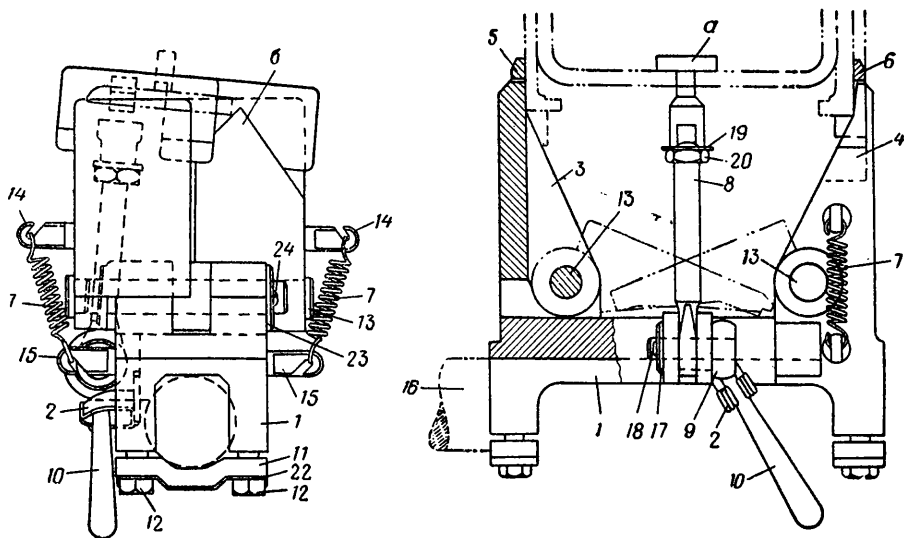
Приспособление для крепления качающейся части миномета по-походному (С615) (вид спереди и слева):
